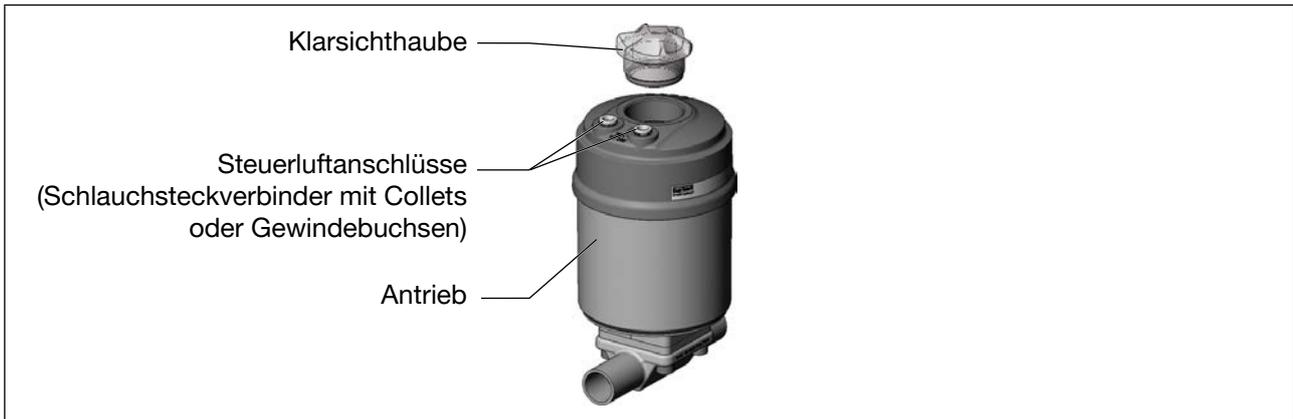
Montage der Schaltspindel bei Prozessventilen des Typs 2103, 2300 und 2301; Klarsichthaube und Steuerluftanschlüsse entfernen
